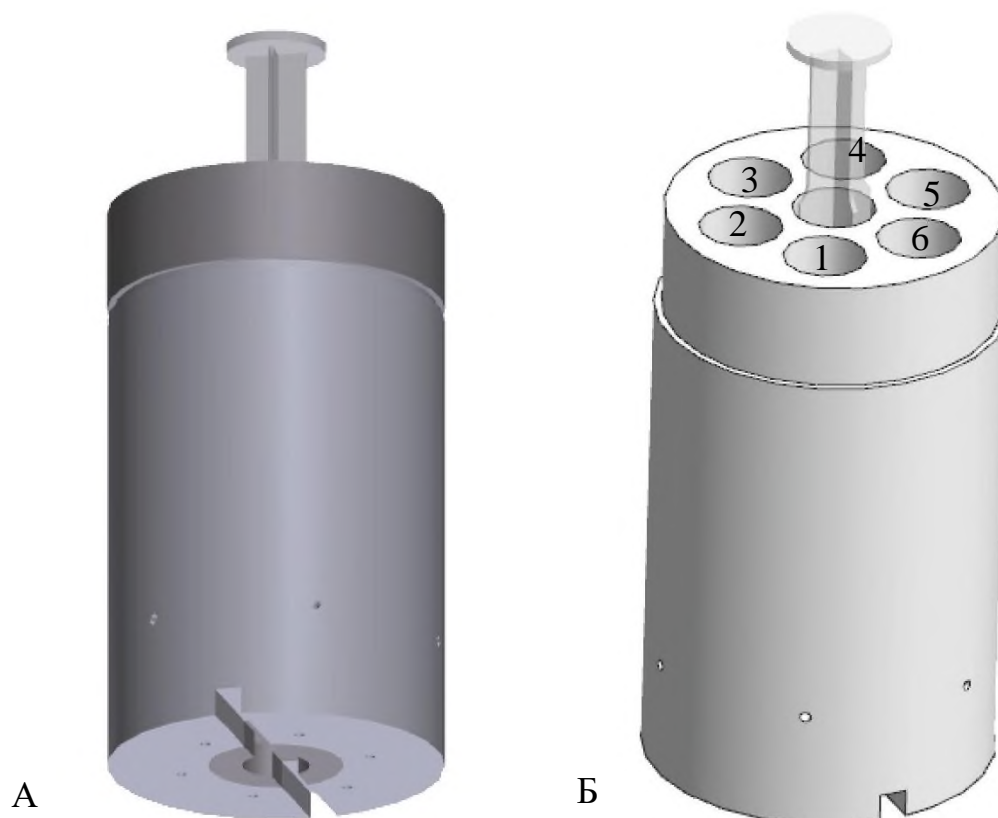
3D модели картриджа: А – вид картриджа в сборе; Б – вид картриджа без крышки
